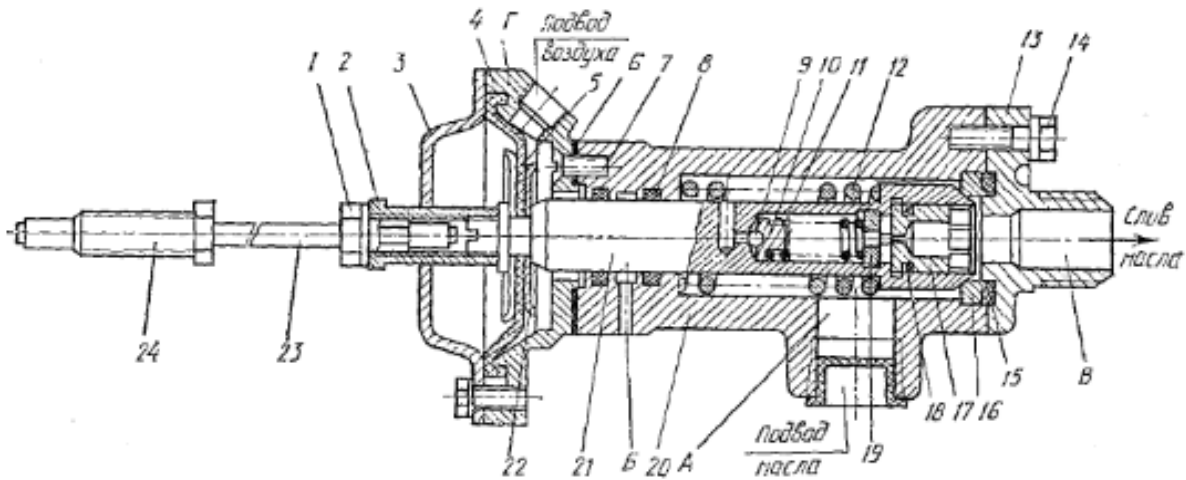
Клапан управления опрокидывающего механизма платформы самосвала МАЗ-5549
